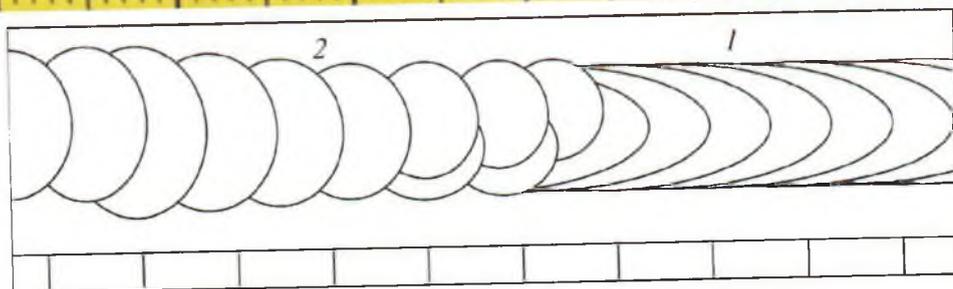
Стыковое сварное соединение обечайки сосуда. Правый участок 1 шва выполнен автоматической сваркой. Левый участок 2 – ремонтный, выполнен ручной дуговой сваркой в среде защитных газов.
